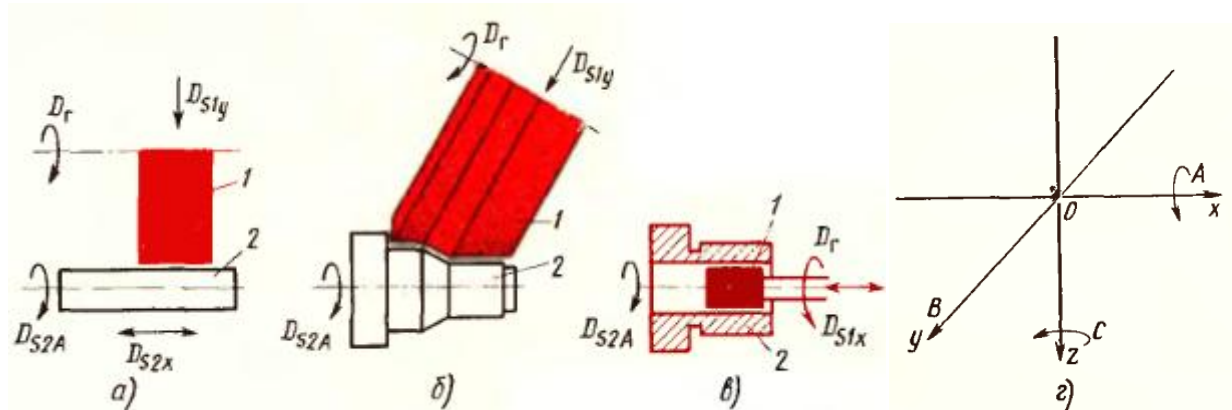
Элементы движений круга (1) и заготовки (2) при шлифовании:
